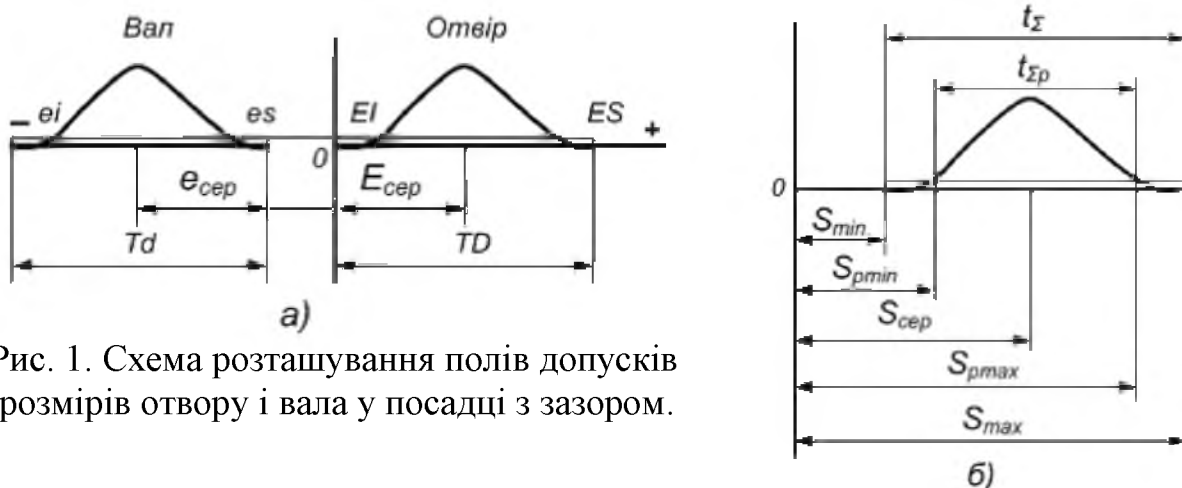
Схема розташування полів допусків розмірів отвору і вала у посадці з зазором.
